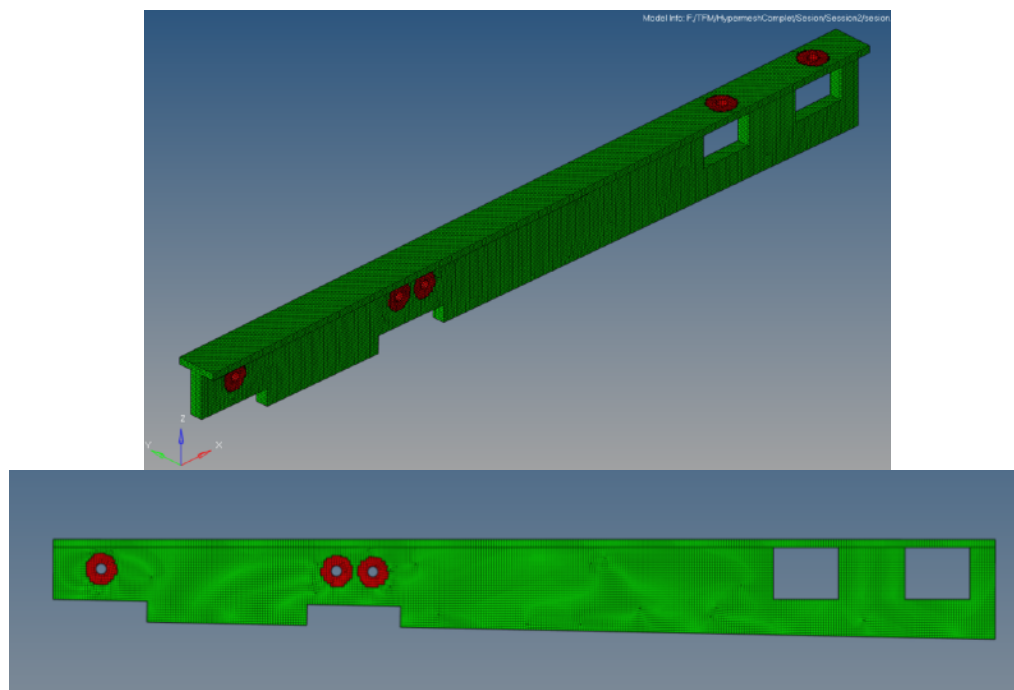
SOPORTE MALLADO CON ELEMENTOS 3D MIXED
